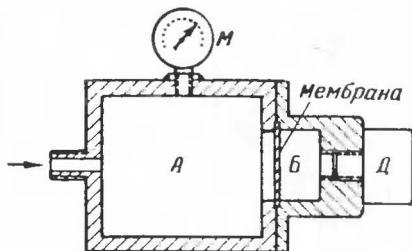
Конструкция приспособления для динамической калибровки датчиков давления.
